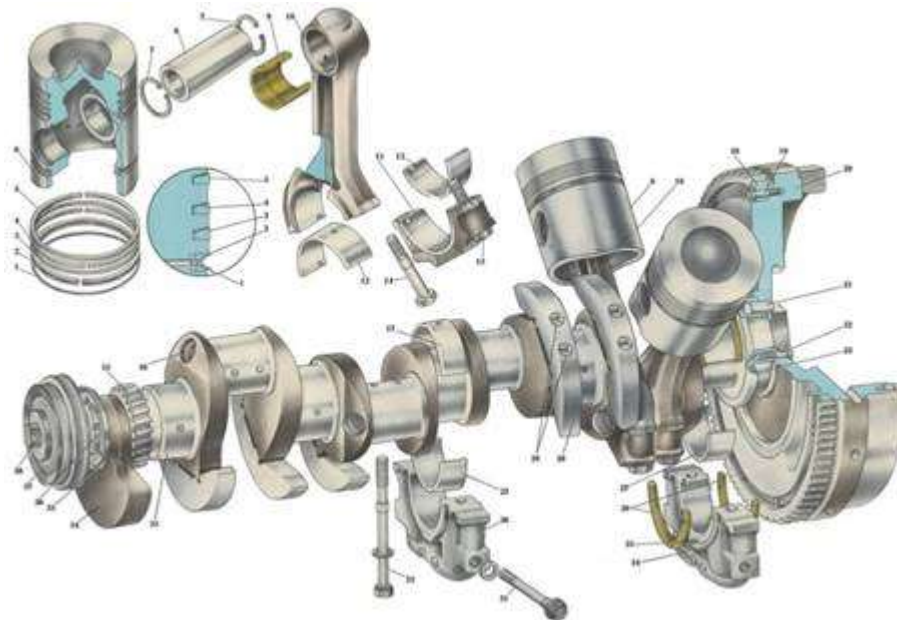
Корбово-гонковий механізм двигуна ЯМЗ-238 (поз. 8 – поршневий палець)
